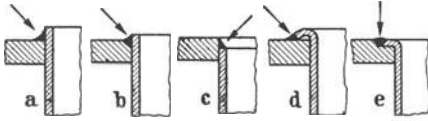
Einschweißen von Rohren in Rohrwände.
